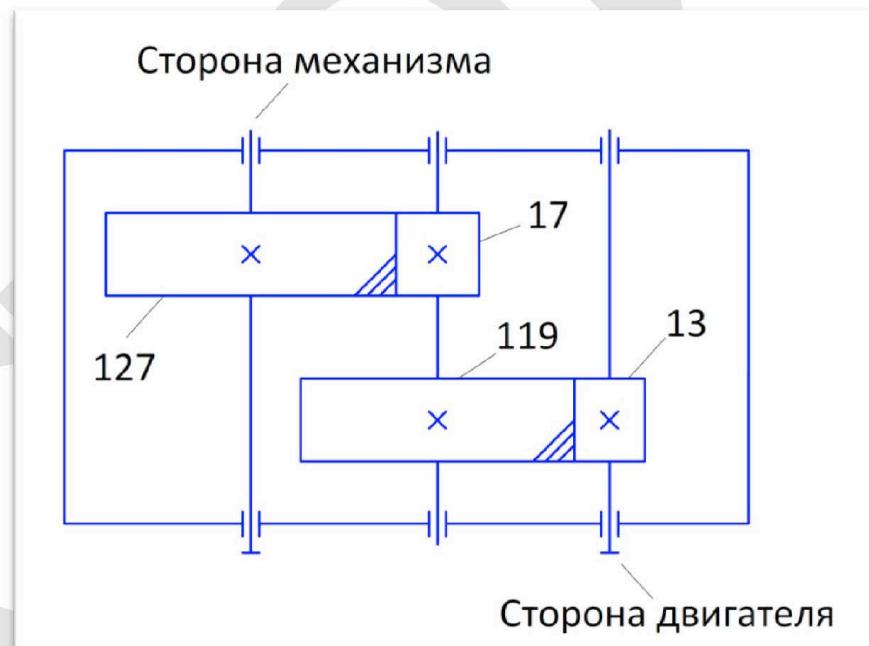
Двухступенчатая передача с указанием количества зубьев каждой шестерни
